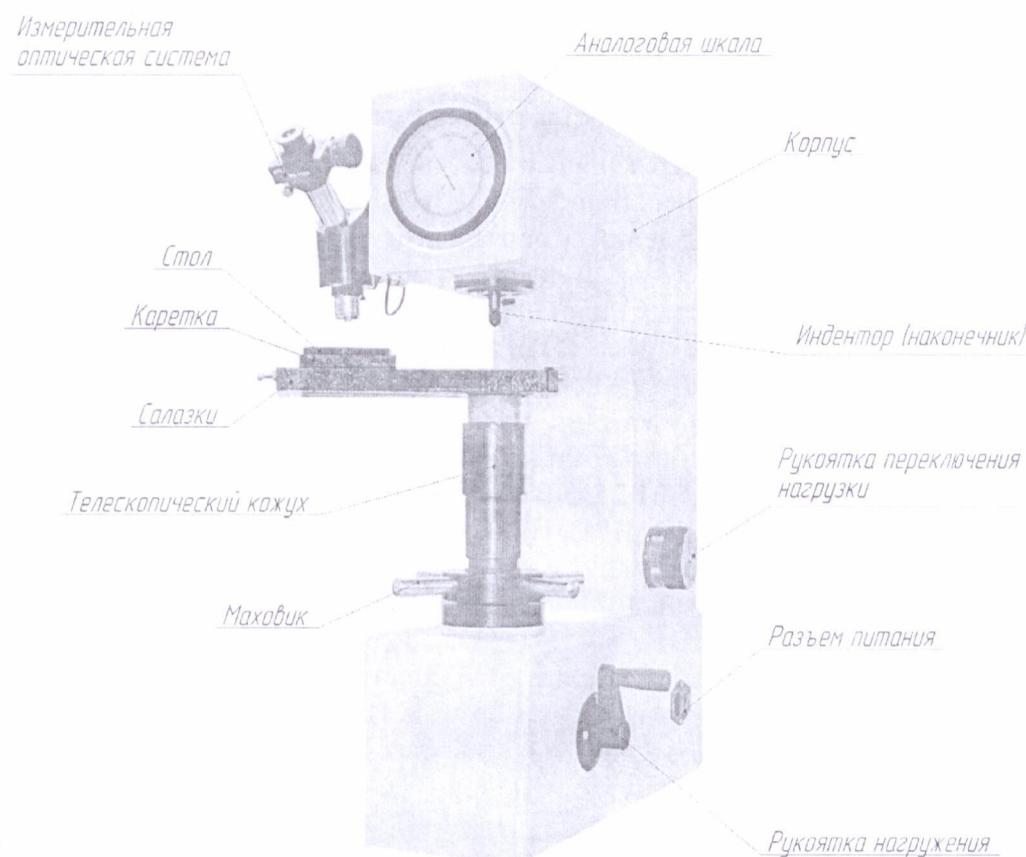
Общий вид твердомера ИТБРВ-М
